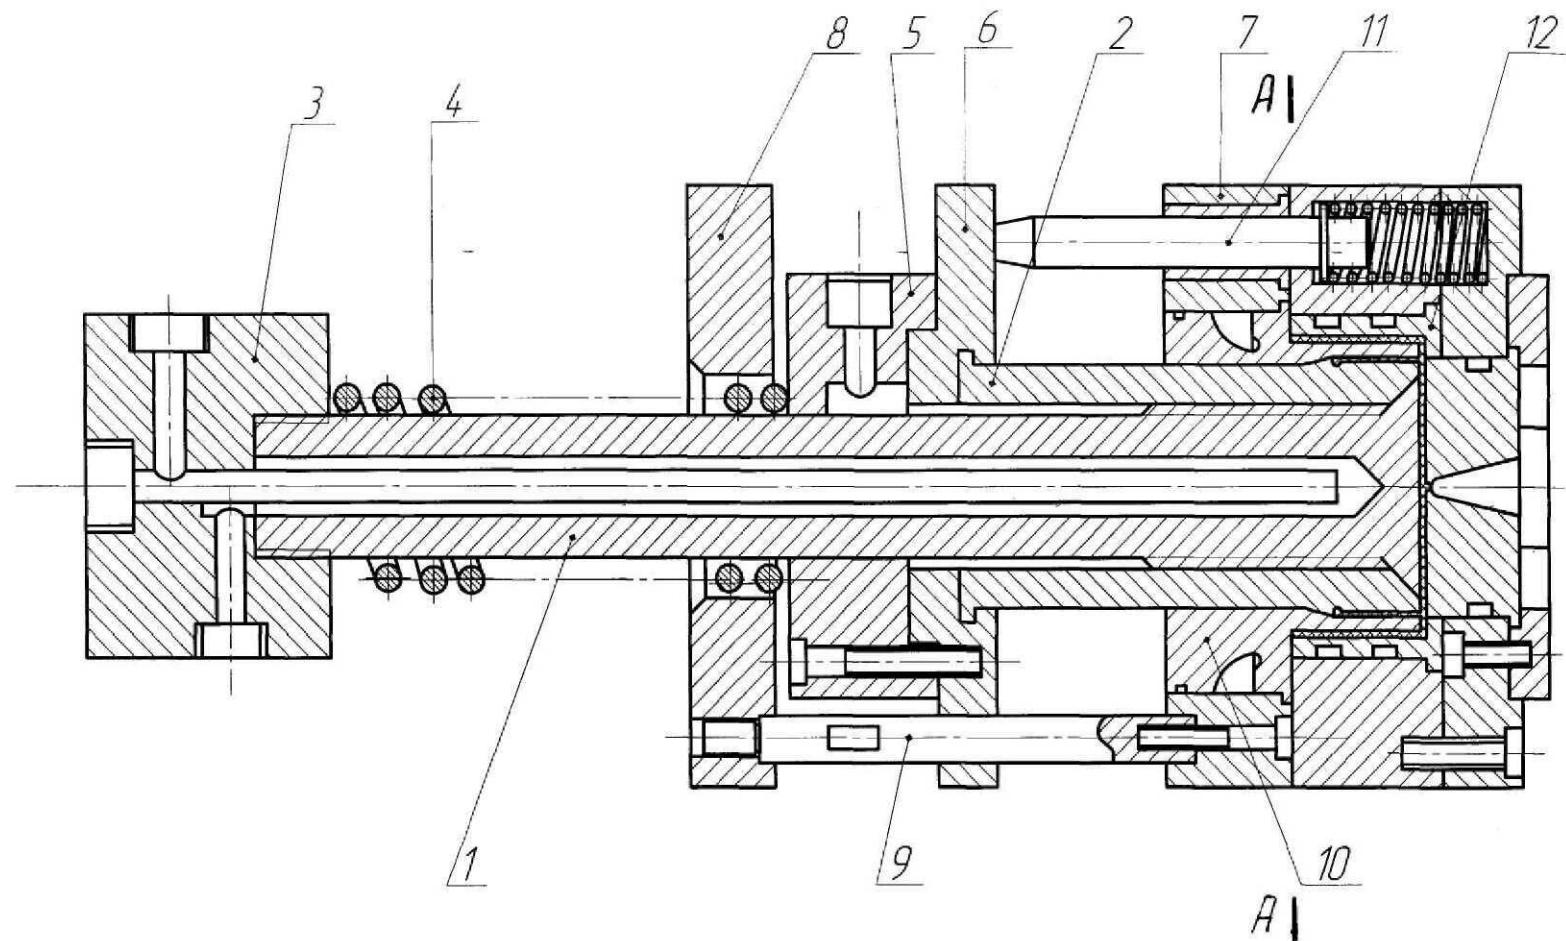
Пресс-форма для изготовления детали «пробка»:
